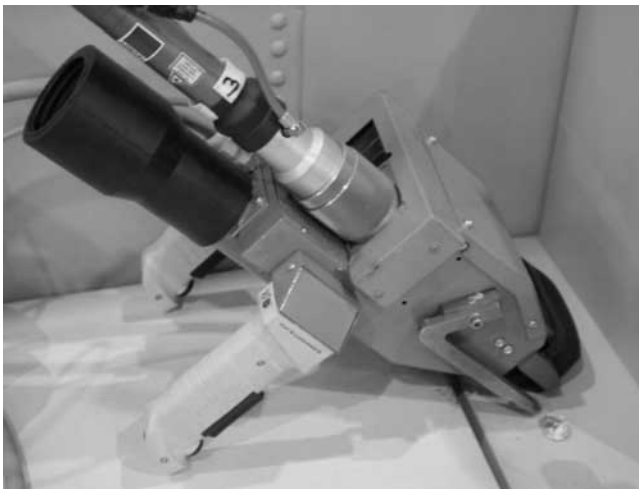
Manuell geführter Laserhandkopf für das Schweißen und Schneiden
